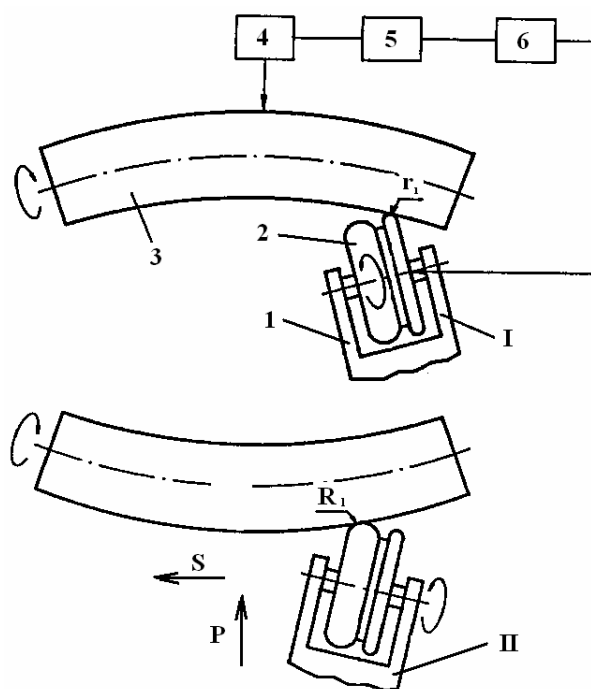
Схемы правки вала с помощью накатной головки и накатного ролика с двумя рабочими профилями
